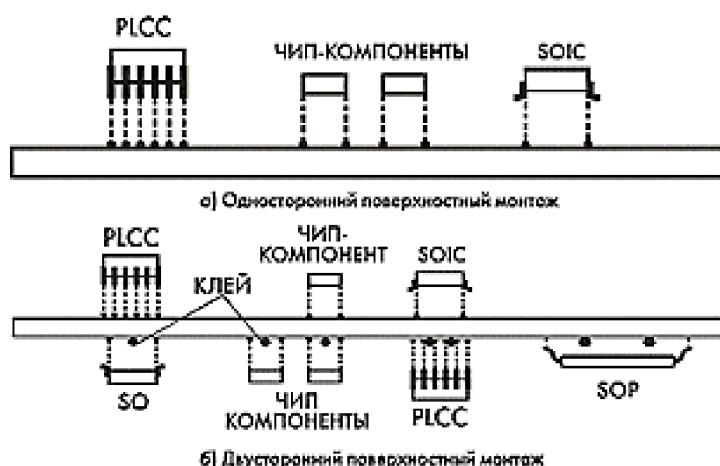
а,б одно- и двусторонний поверхностный монтаж
